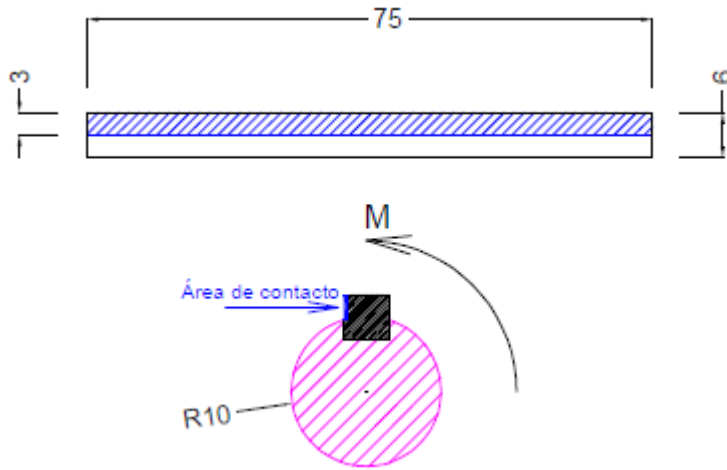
Aplastamiento. Eje de diámetro 20 mm.
